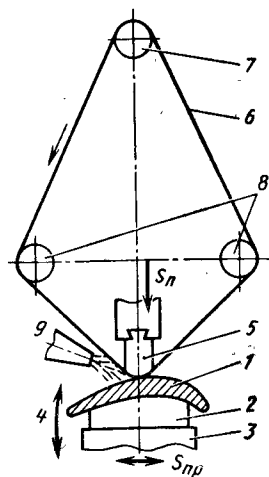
Схема шлифования спинки пера рабочей лопатки турбины:
